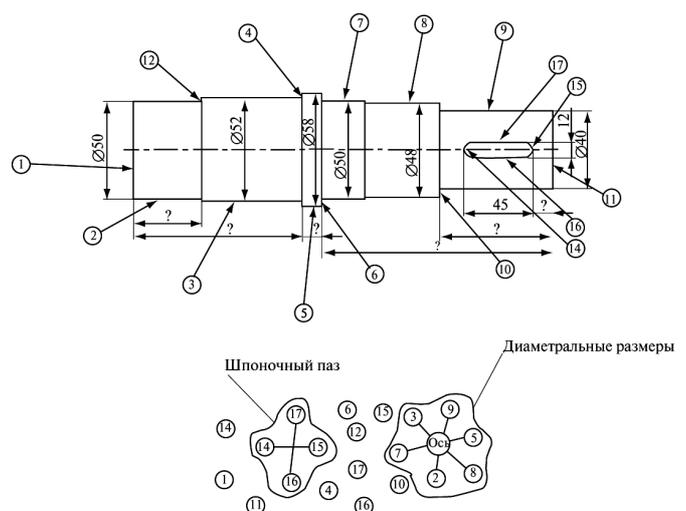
Чертеж детали после простановки размеров на конструктивные элементы
